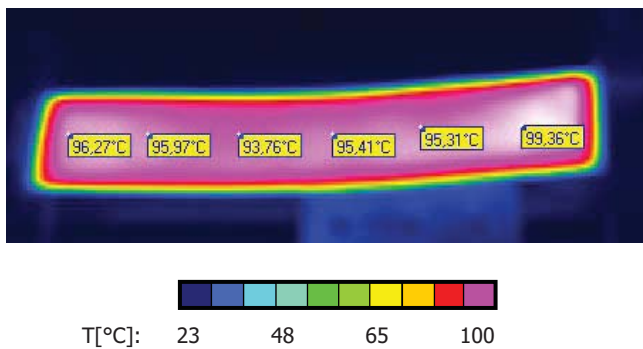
Infrarotaufnahmen der Schweißelementerwärmung
